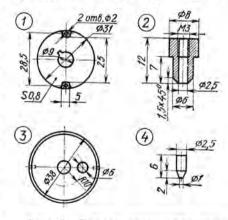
Детали дополнительного токосъемника: 1 — шайба: 2 — шеткодержатель; 3 — доработка подшипникового щита; 4 - щетка.
